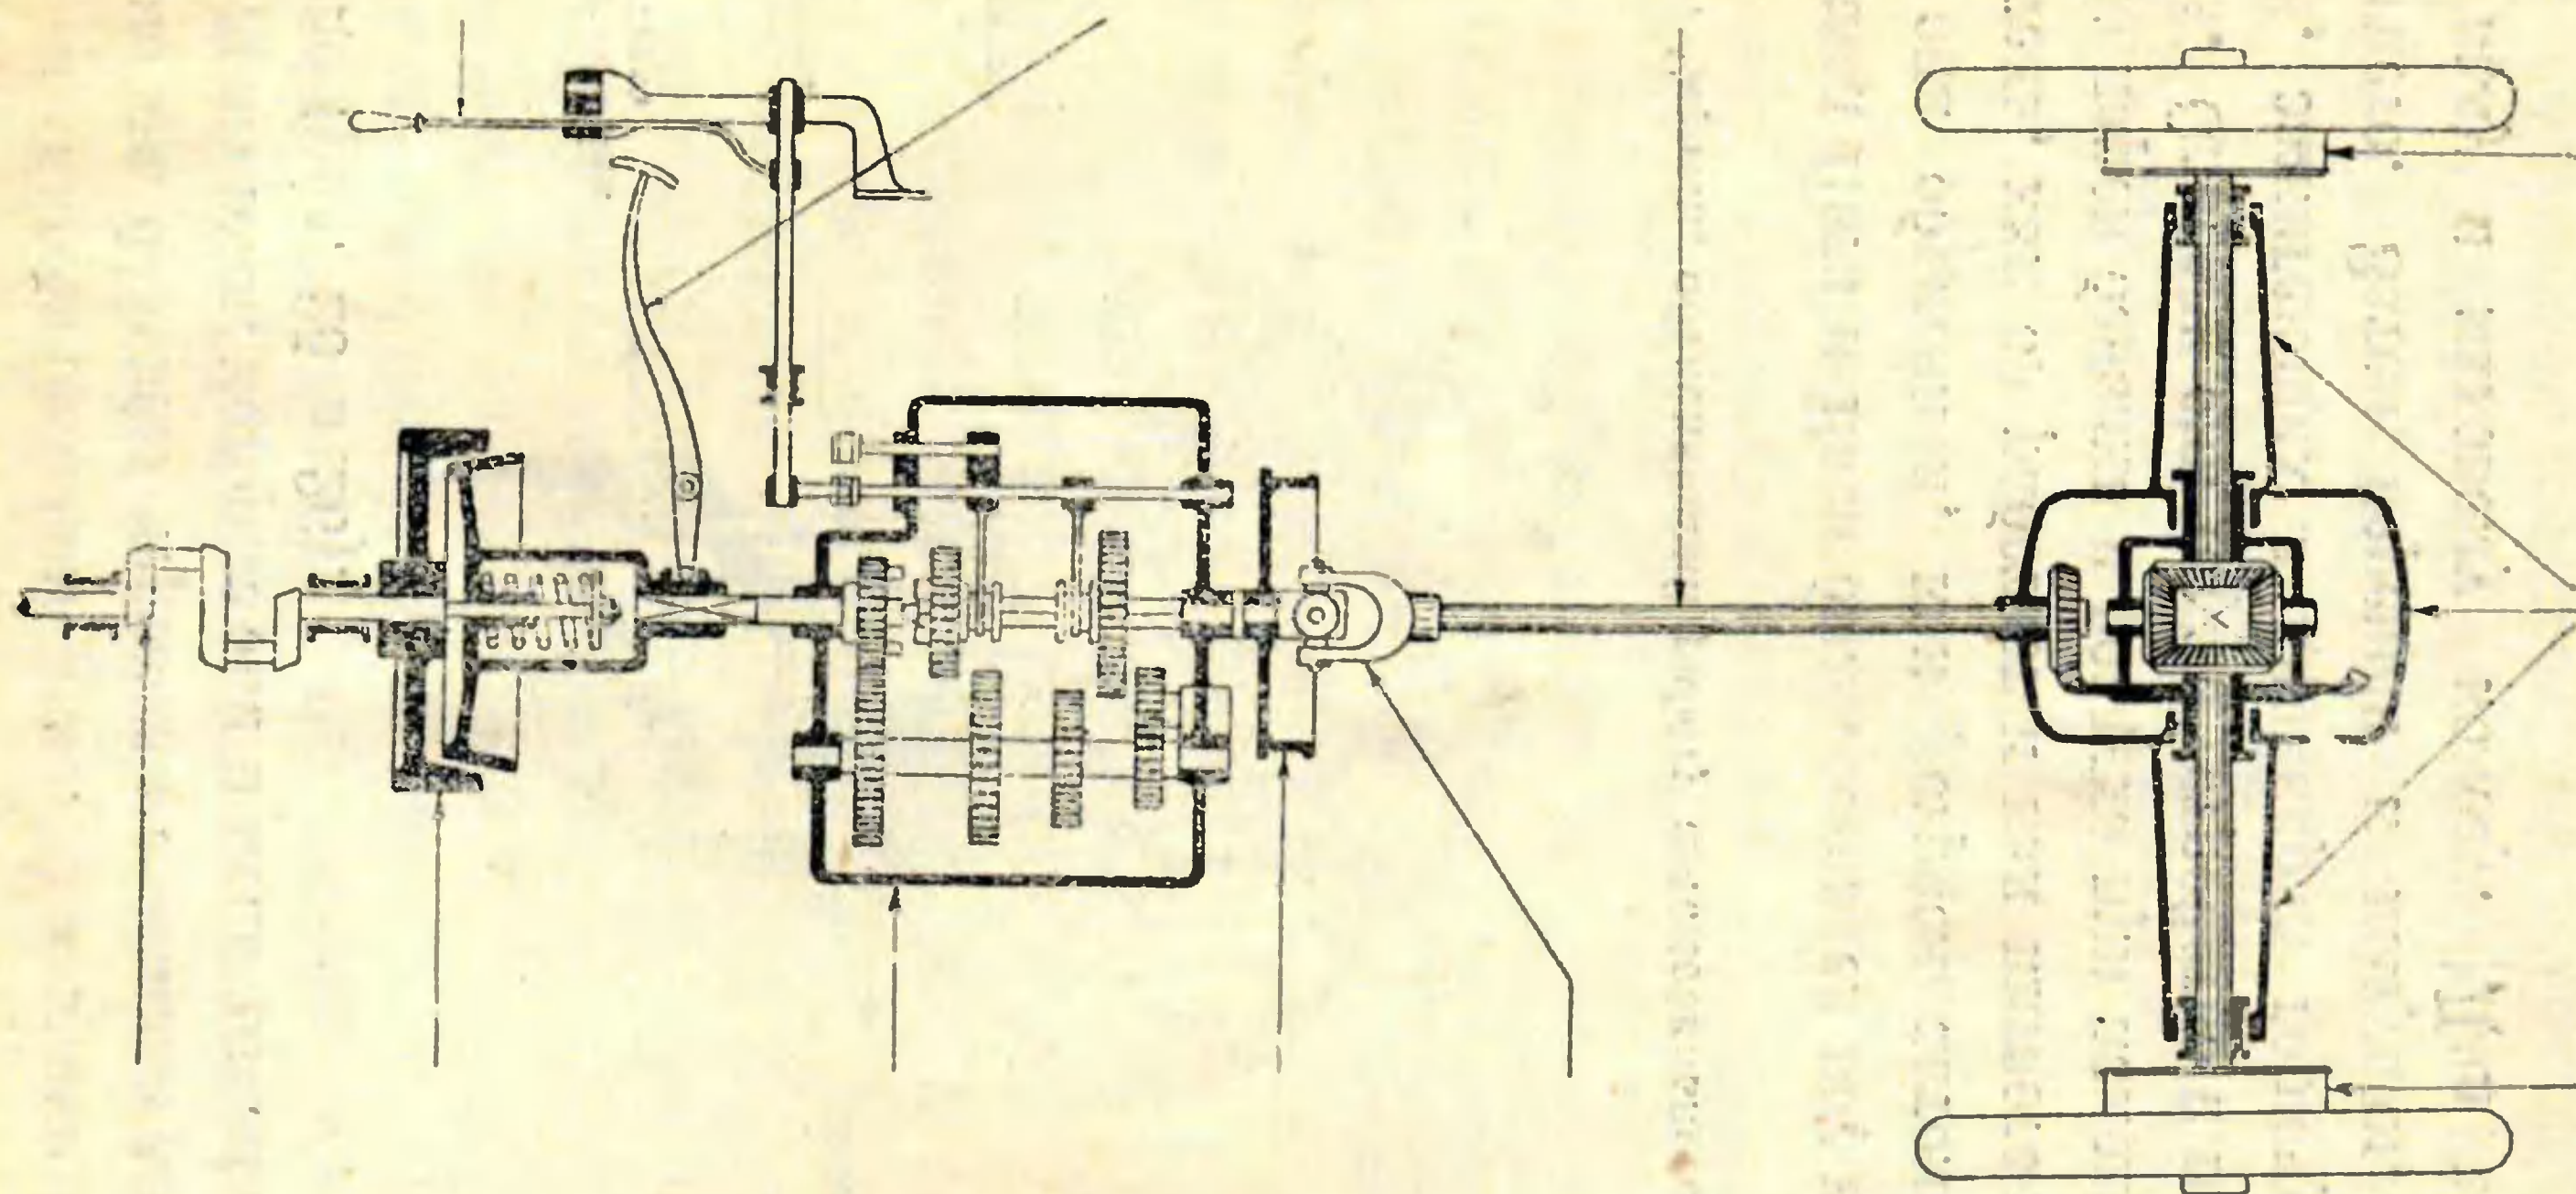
Чертеж, показывающий, как передается движение двигателя колесам автомобиля.
